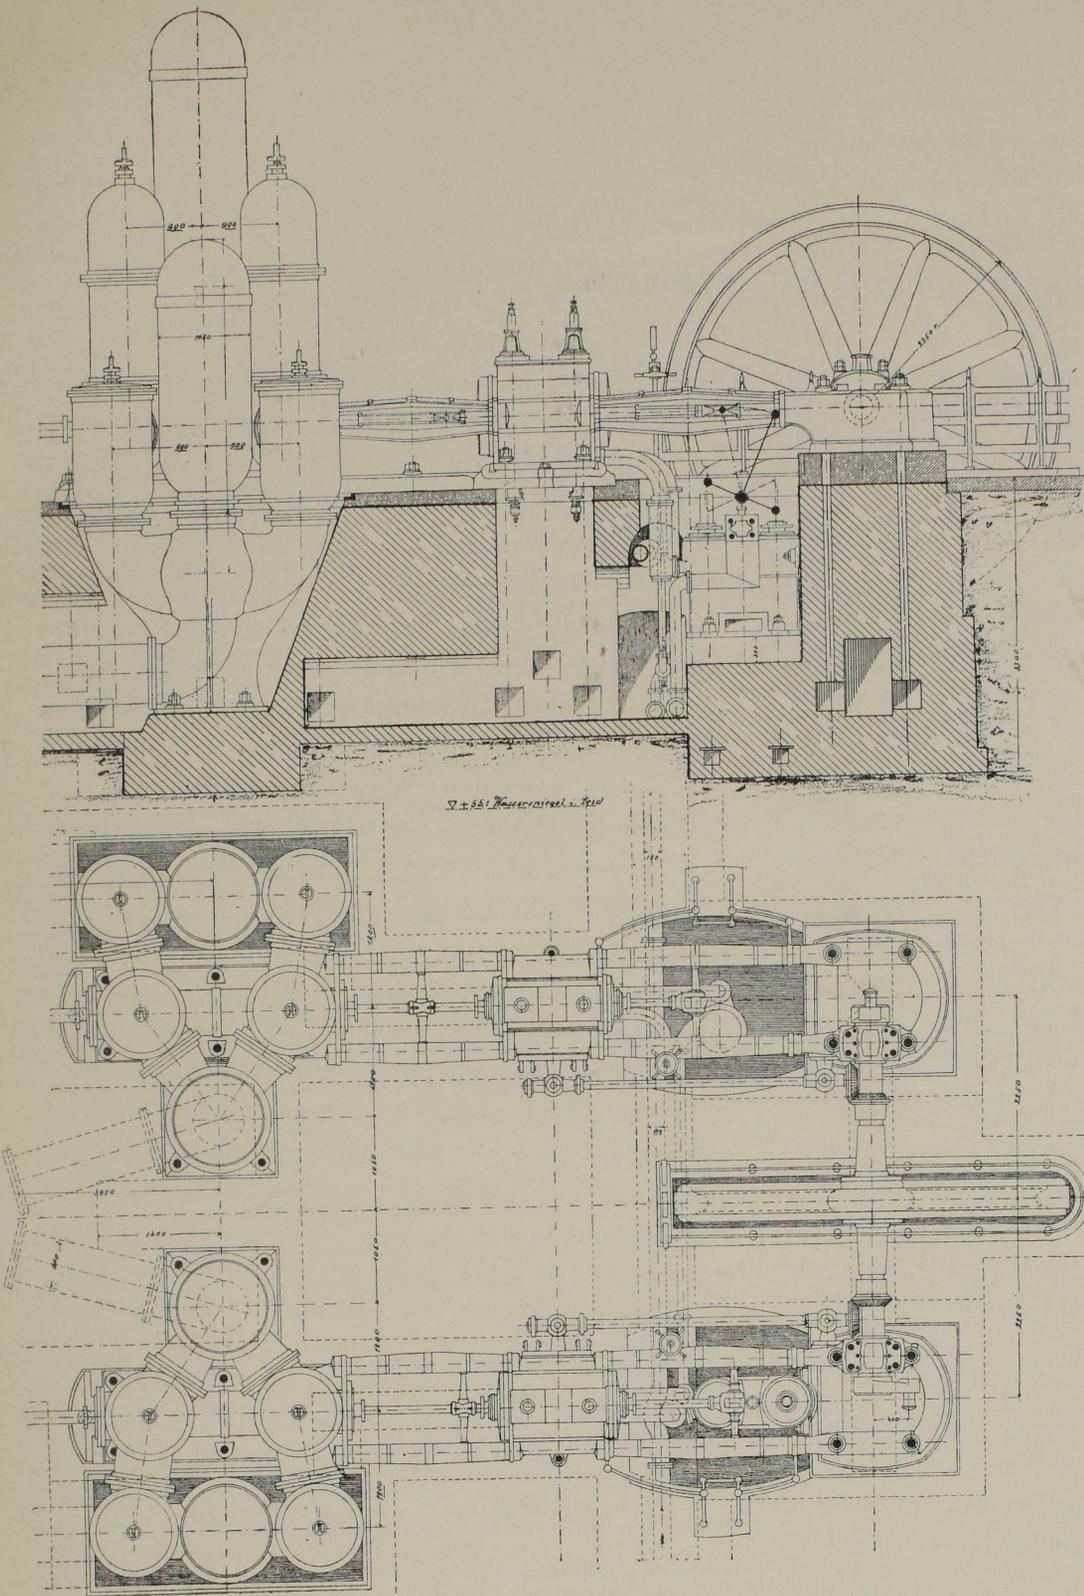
Seitenansicht und Grundriss der Pumpmaschine. Massst. 1:80.
